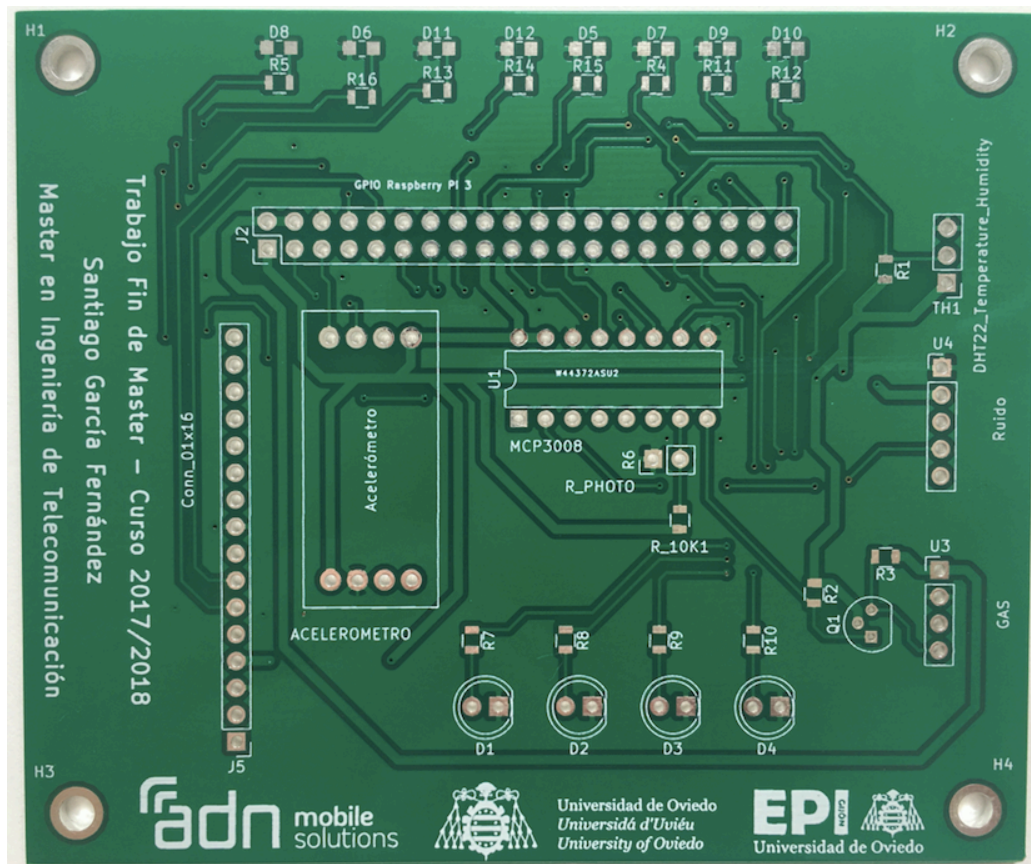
Imagen de capa top de la PCB real una vez fabricada.
